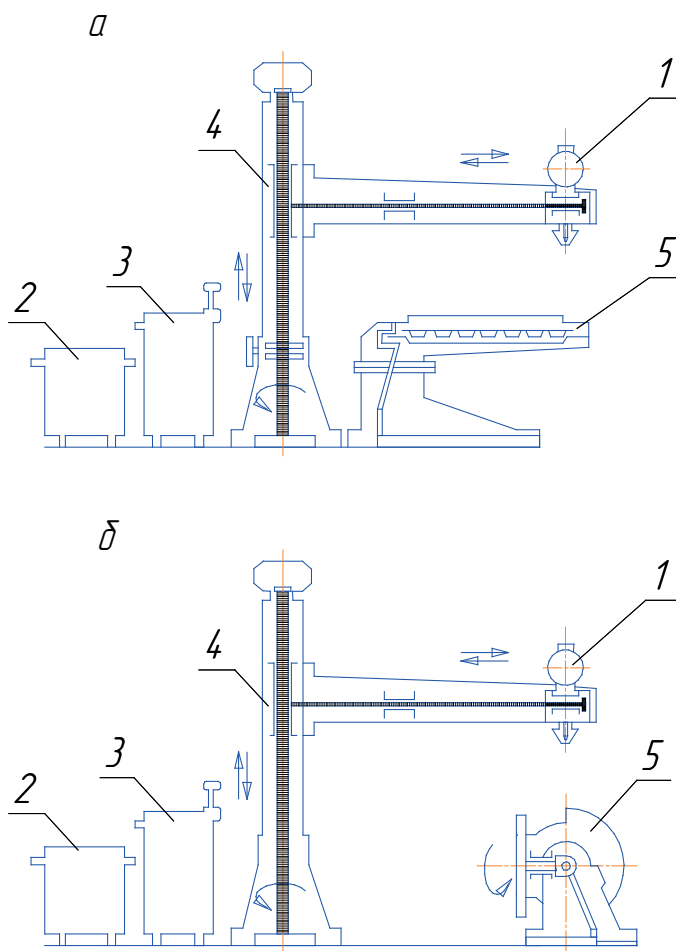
Типовые компоновки установок для сварки продольных (а) и кольцевых (б) швов:
